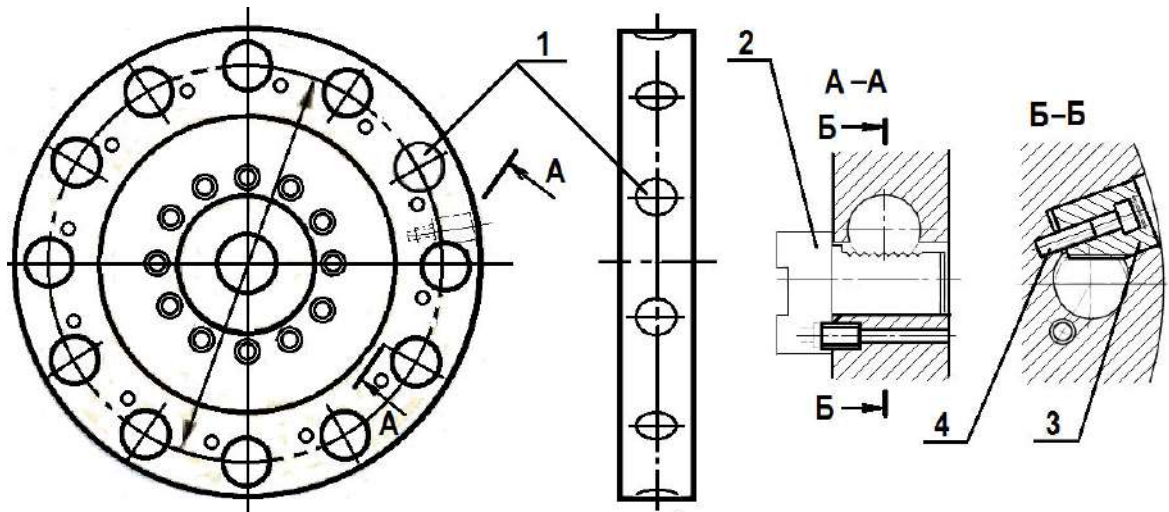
Диски інструментальні для револьверних головок (форма оправок VDI)
